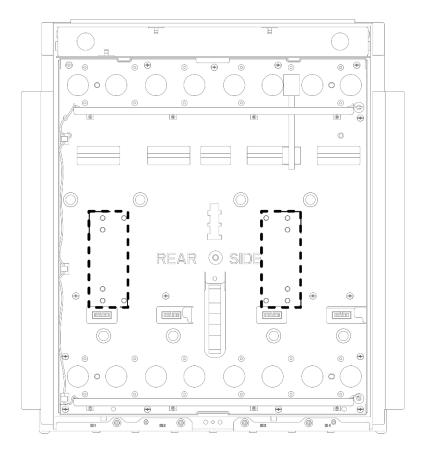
Ubicación de los pernos para instalar las asas de elevación
